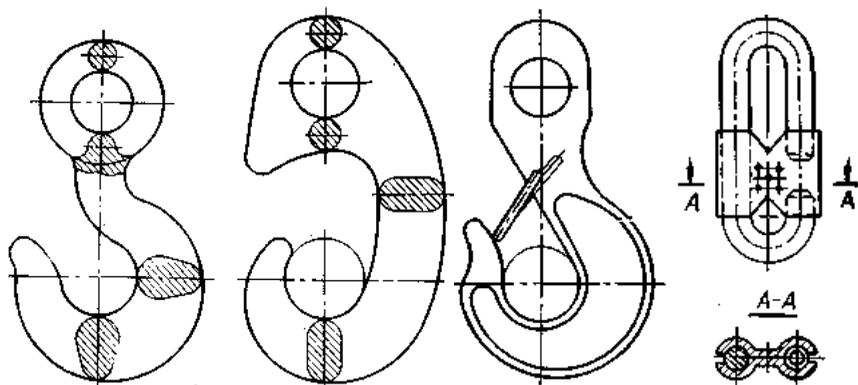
Звенья для навешивания на крюк грузоподъемной машины:
